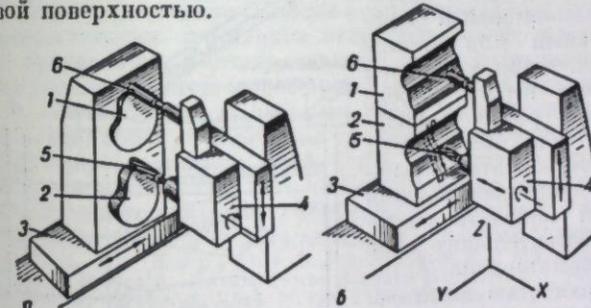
Схема движения подачи: 1 — копира; 2 — изделие; 3 — стол; 4 — шпиндельная бабка; 5 — фреза; 6 — палец; а — плоское копирование; б — пространственное копирование.
